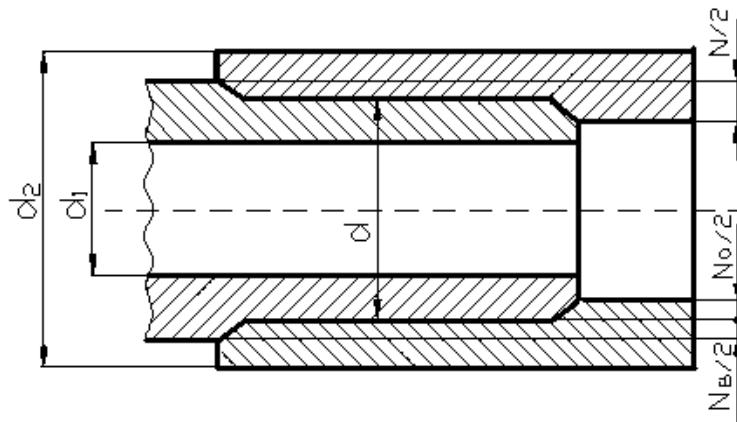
Принципова розрахункова схема складання з'єднання з натягом
